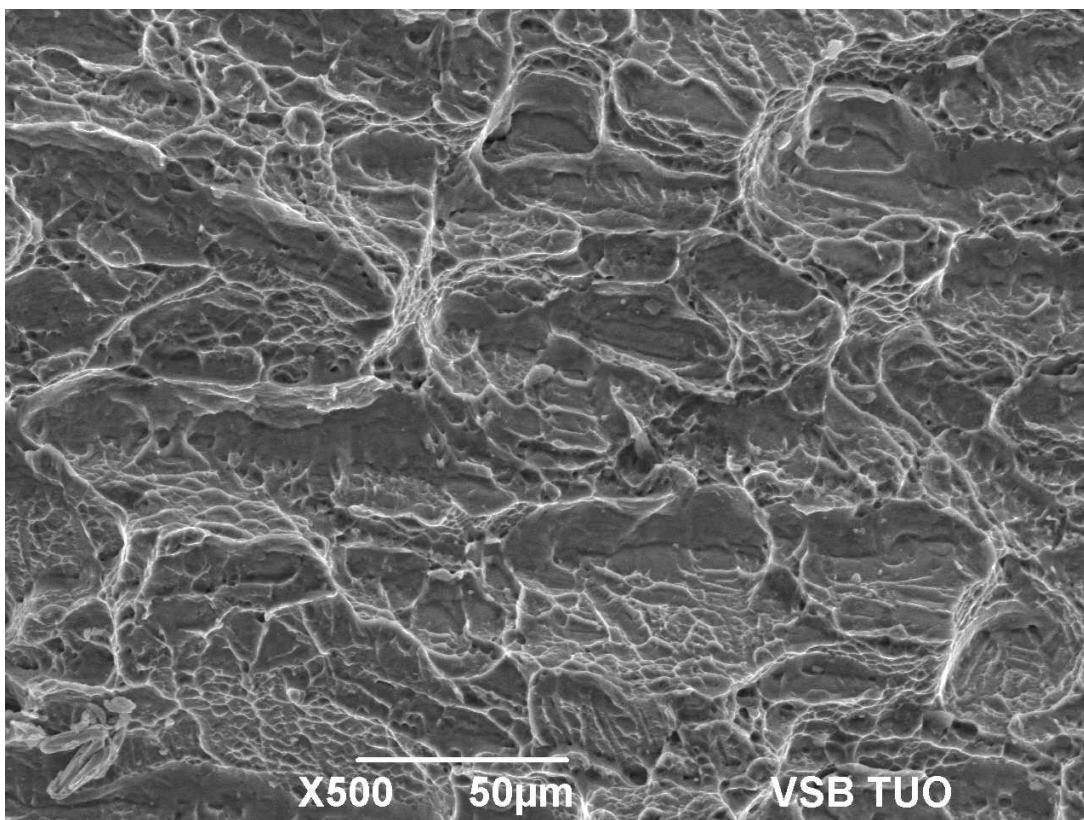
Detail Obr. 36 - houževnatý jamkový lom, střed vzorku
